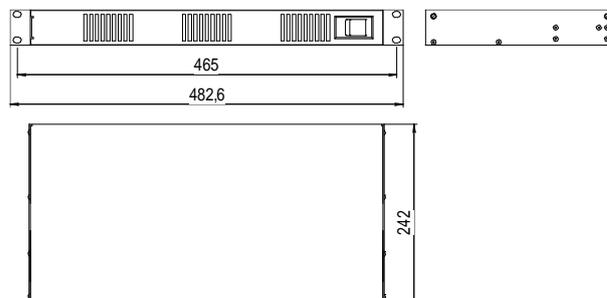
Габаритный чертеж ЩРЗ-7
